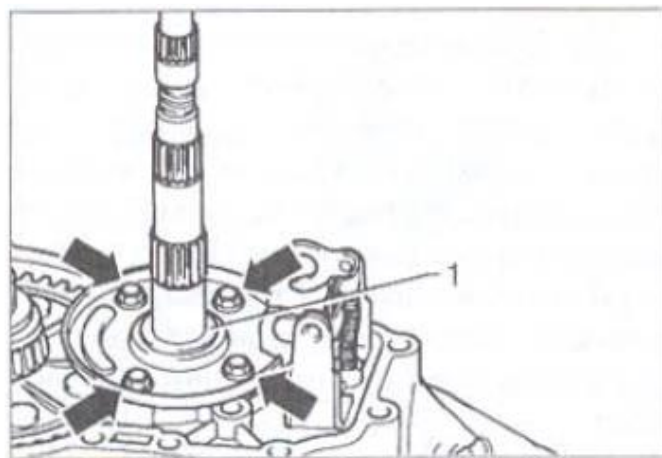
Розташування болтів підшипника первинного вала
